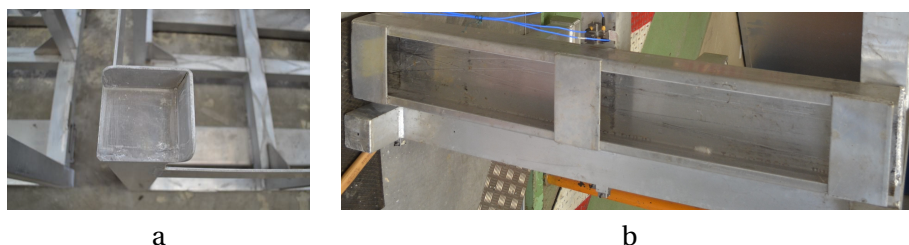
Photos d'un avaloir (a) et d'une barre de passage des fourches (b)
